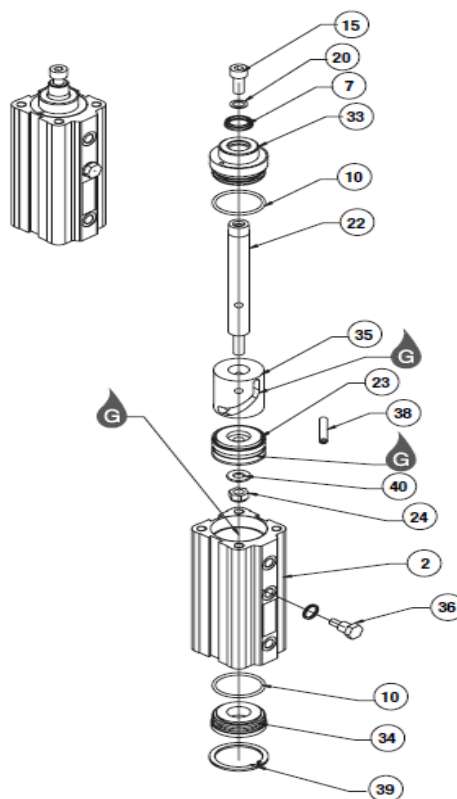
Řez pneumatickou otočnou upínkou
